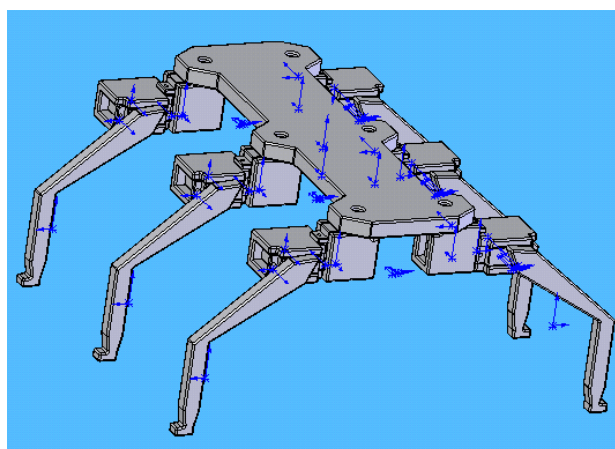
Vista Frontal Conjunto Pata-Hombro-Cuerpo
